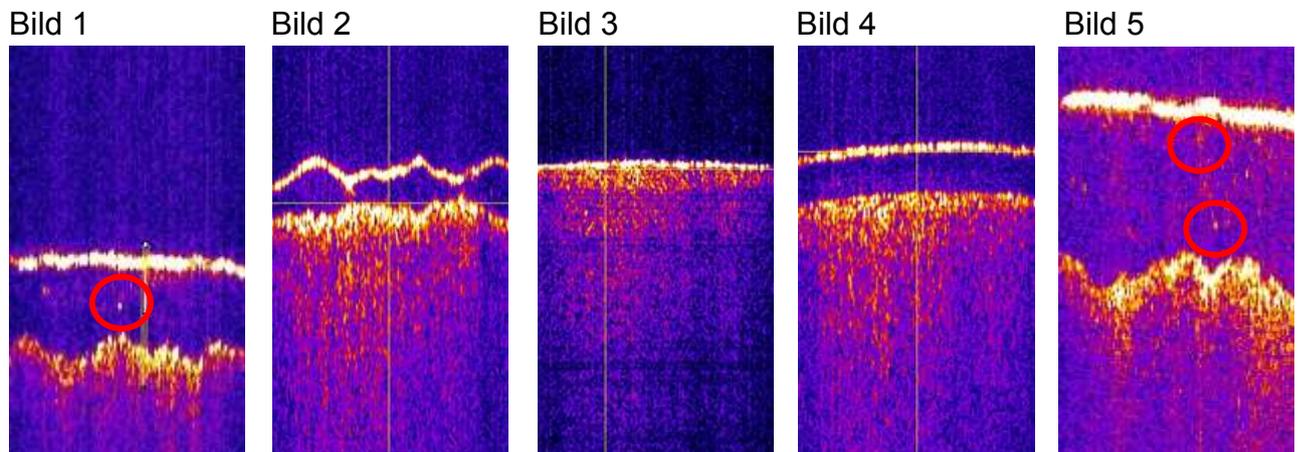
→ Lackschicht mit eingebauten Korundpartikeln.
